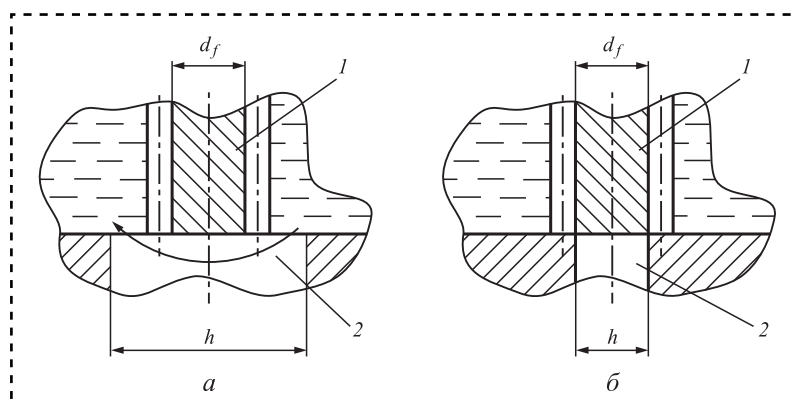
Размеры каналов, выполняемых в цилиндрической зубчатой поверхности солнечной шестерни:
